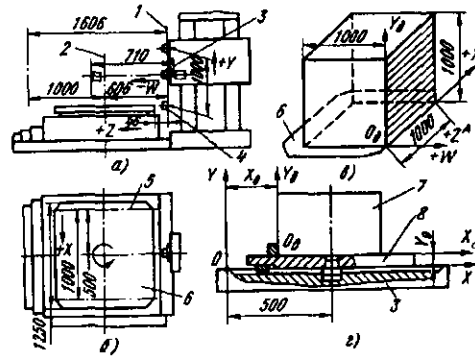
Технологическая зона обработки на станке мод. 2Б622МФ2: а – вид на станок сбоку; б – вид на стол сверху; в – условное изображение зоны обработки (O_d – начало системы координат детали); г – схема установки приспособления и заготовки: 1 – торец полого шпинделя; 2 – ось поворота стола (начало отсчета перемещений стола вдоль оси Z); 3 – начало перемещений шпинделя по оси W ; 4 – начало отсчета перемещений бабки по оси Y ; 5 – начало отсчета перемещений стола поперек станка (по оси X); б – стол станка; 7 – заготовка; 8 – приспособление
